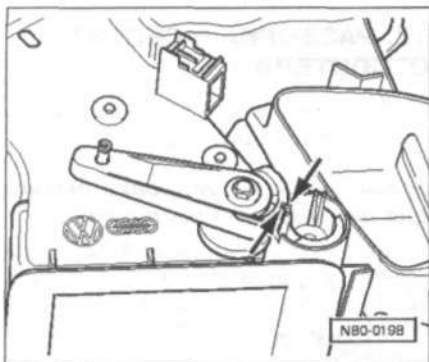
Установка и регулировка рычага для центральной заслонки.
